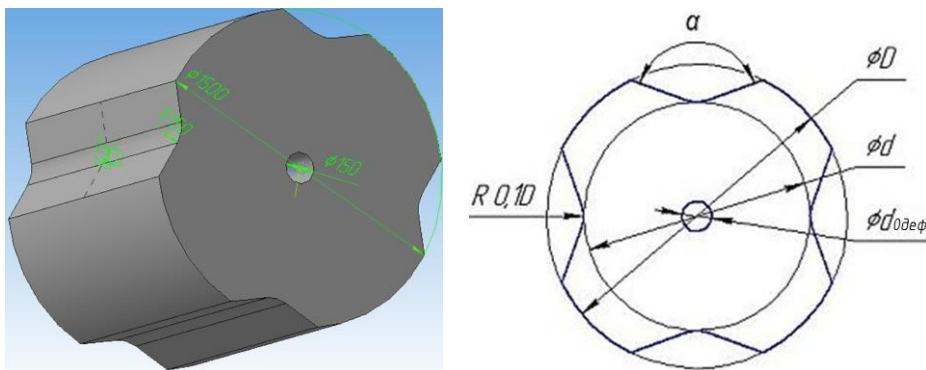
3D модель та поперечний переріз чотирипроменевої заготовки
